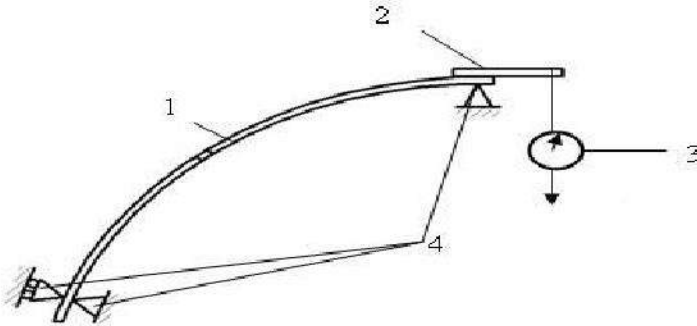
Схема випробування зварювального шва на міцність: 1-остов; 2-ремонтна вставка; 3-динамометр; 4-опора
